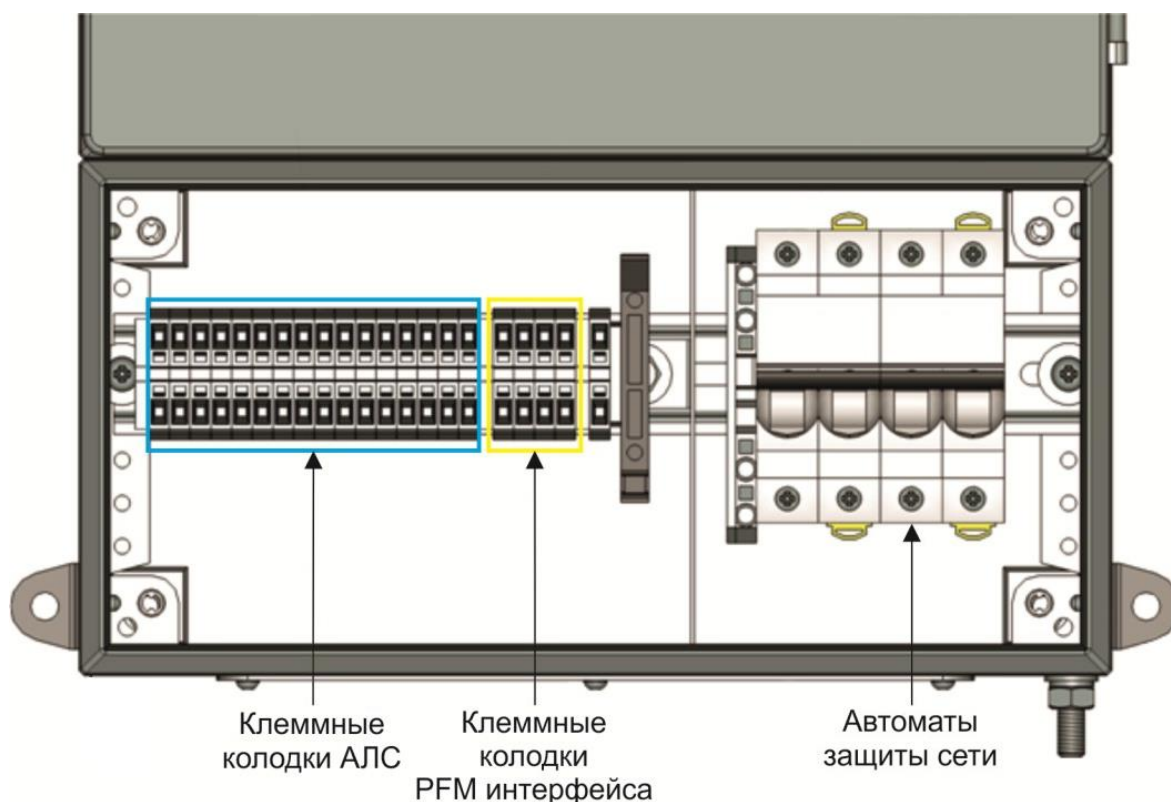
Внешний вид КАУ со снятой нижней крышкой
